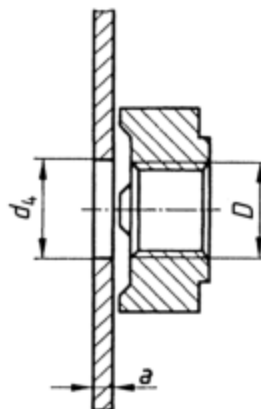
Anschlussmaße (Mutter noch nicht angeschweißt)
